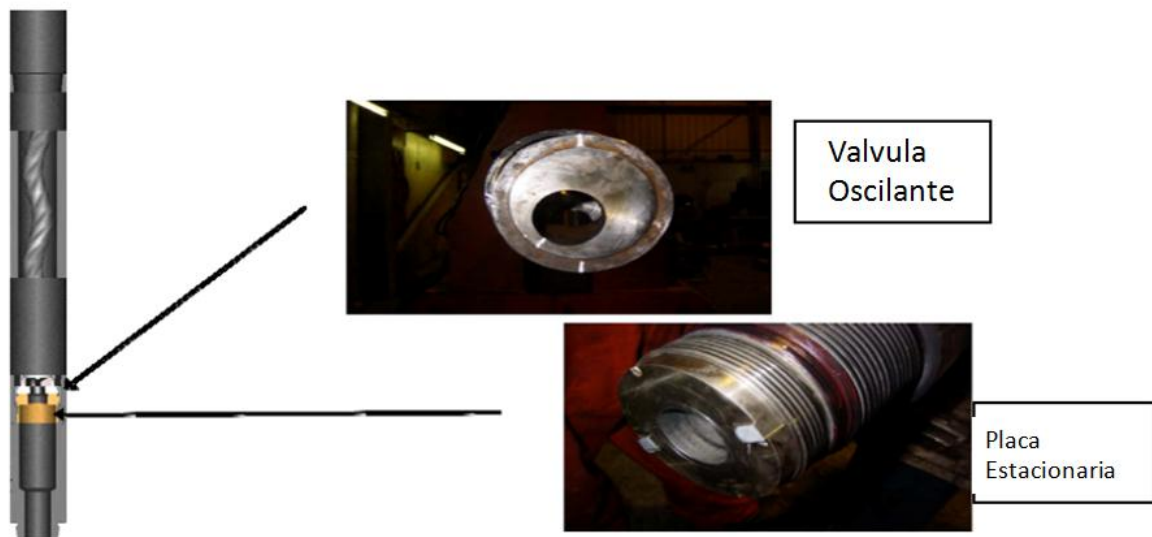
Herramienta Drilling Agitator (DAT)⁸
